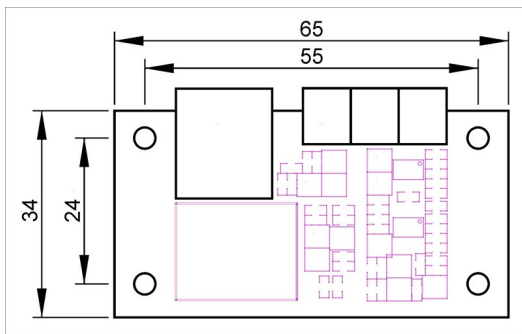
Габаритный чертеж модуля сопряжения THC2-DV1
